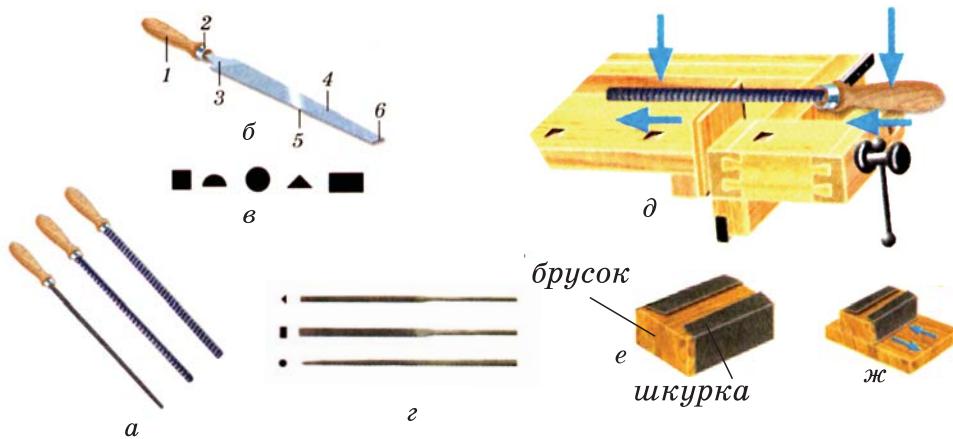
Инструменты и приспособления для зачистки деталей из древесины:
